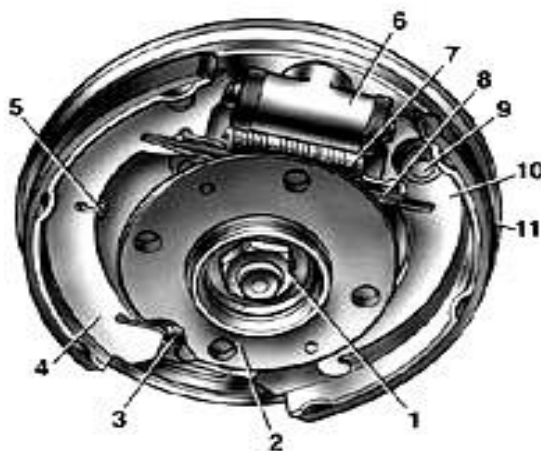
Барабанный тормозной механизм: 1 – гайка крепления ступицы; 2 – ступица колеса; 3 – нижняя стяжная пружина колодок; 4 – тормозная колодка; 5 – направляющая пружина; 6 – колесный цилиндр; 7 – верхняя стяжная пружина; 8 – разжимная планка; 9 – палец рычага привода стояночного тормоза; 10 – рычаг привода стояночного тормоза; 11 – щит тормозного механизма
